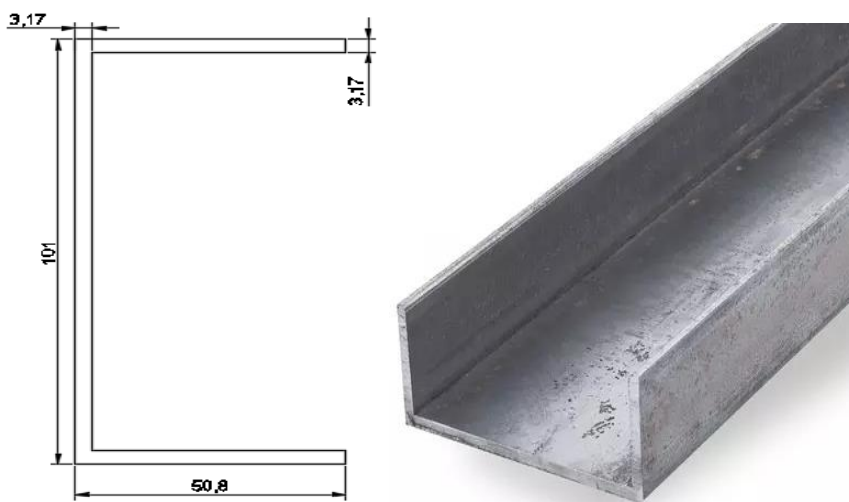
Perfil o canal tipo C de fierro galvanizado para la estructura (Elaboración propia).
